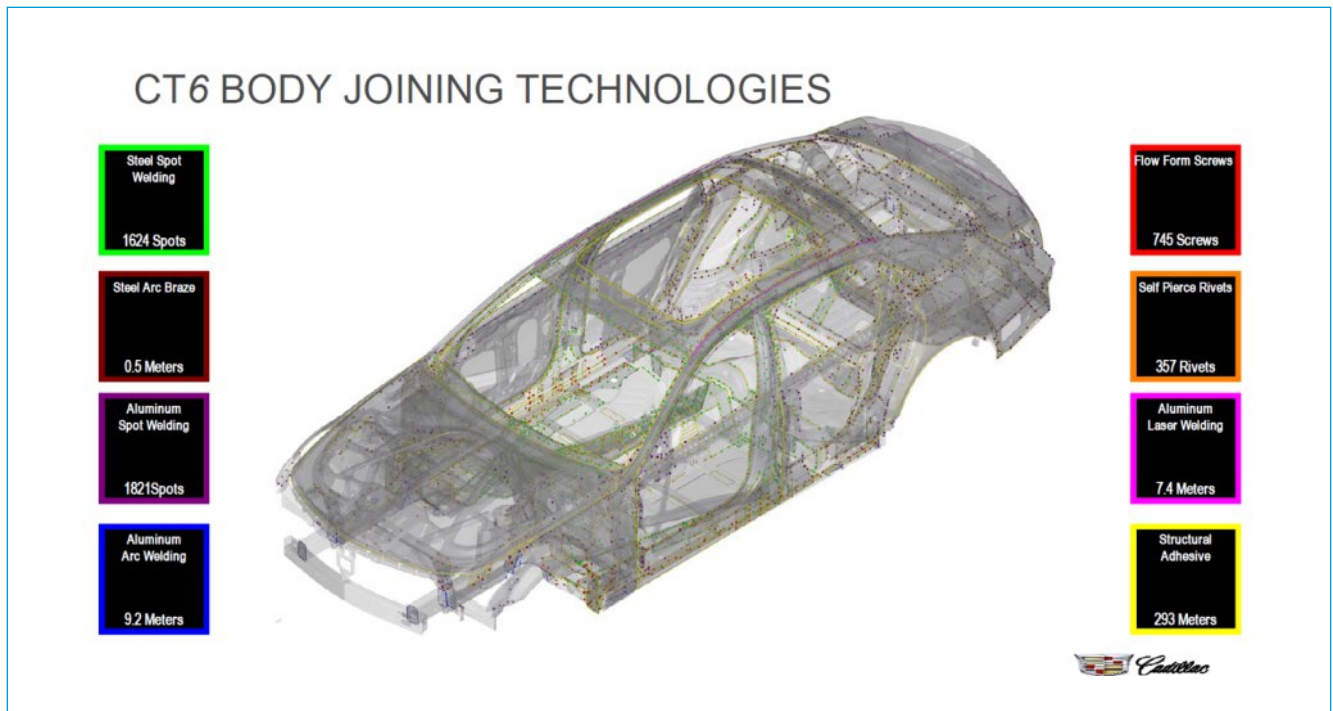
// In diesem Fahrzeug verwendete Füge-technologie. Darunter findet man auch 745 ARNOLD Flowform[®]-Schrauben.
